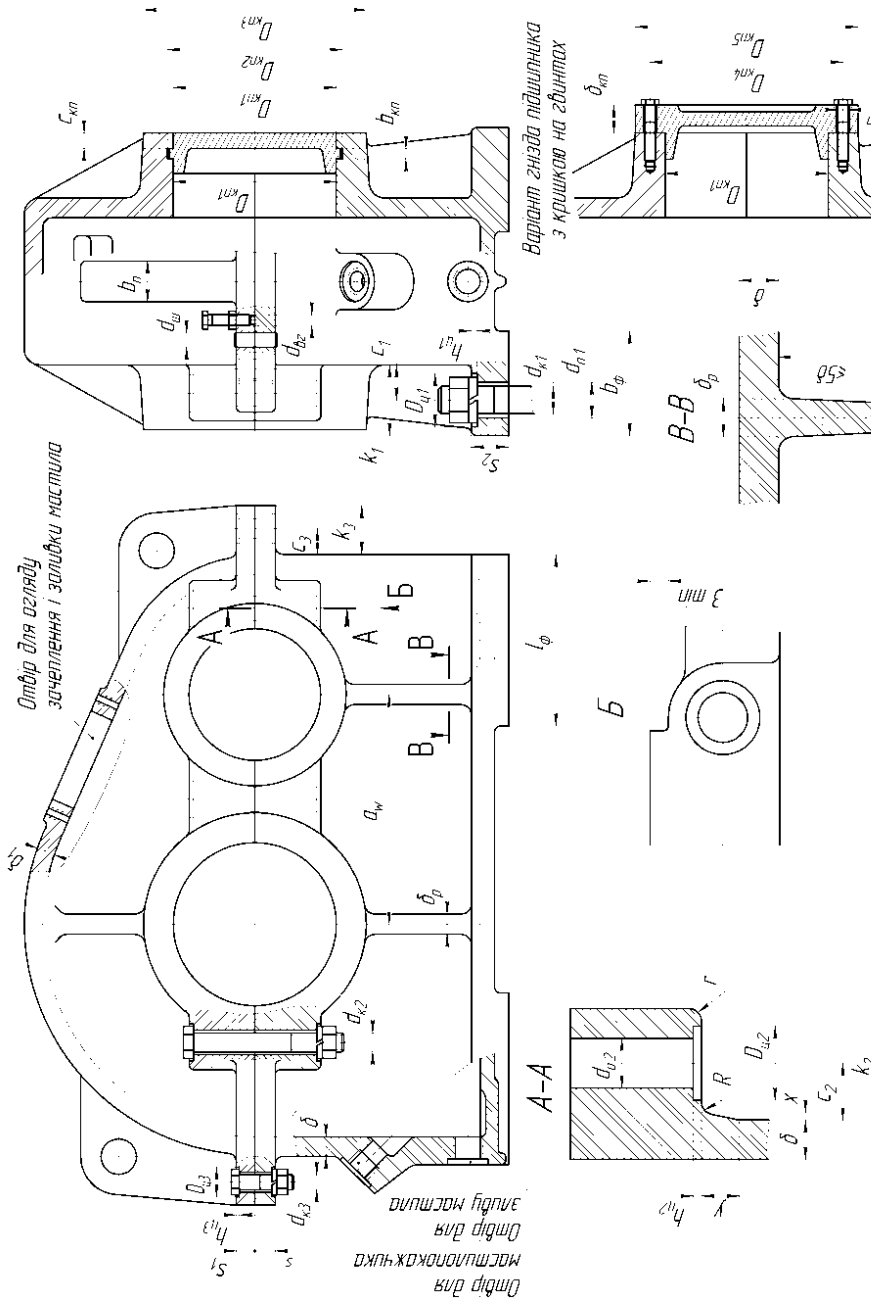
Конструктивні елементи корпусу і кришки редуктора
